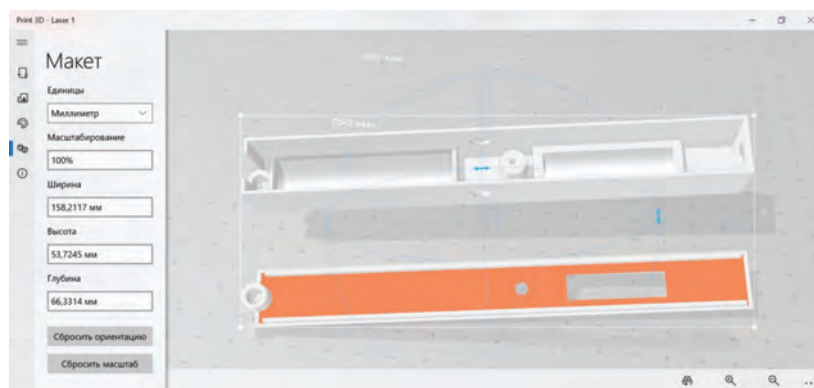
3D-модели корпуса и крышки лазерного указателя
